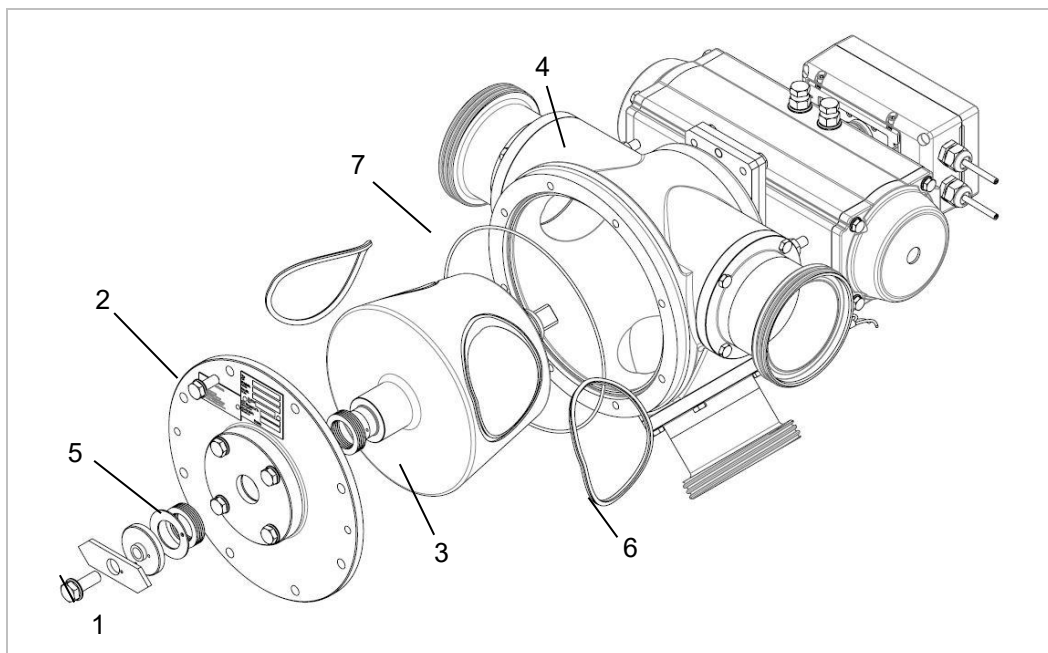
démonter le couvercle latéral du WYK et retirer le rotor
